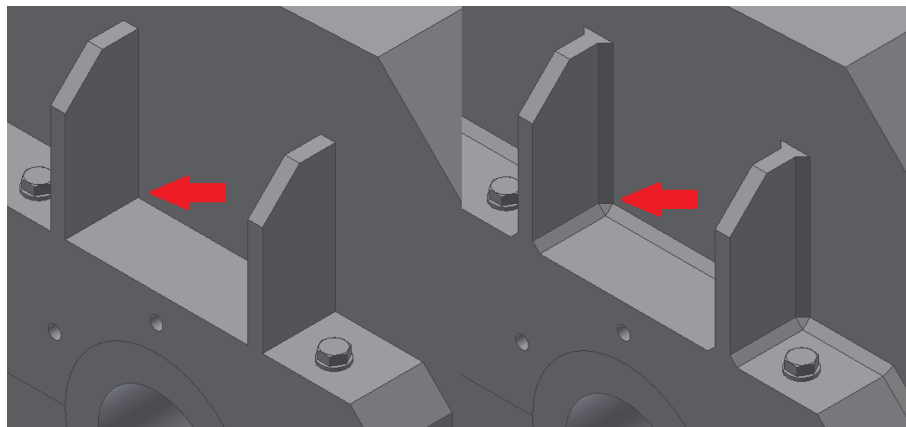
Detalle geométrico de la ausencia y presencia del cordón de soldadura
